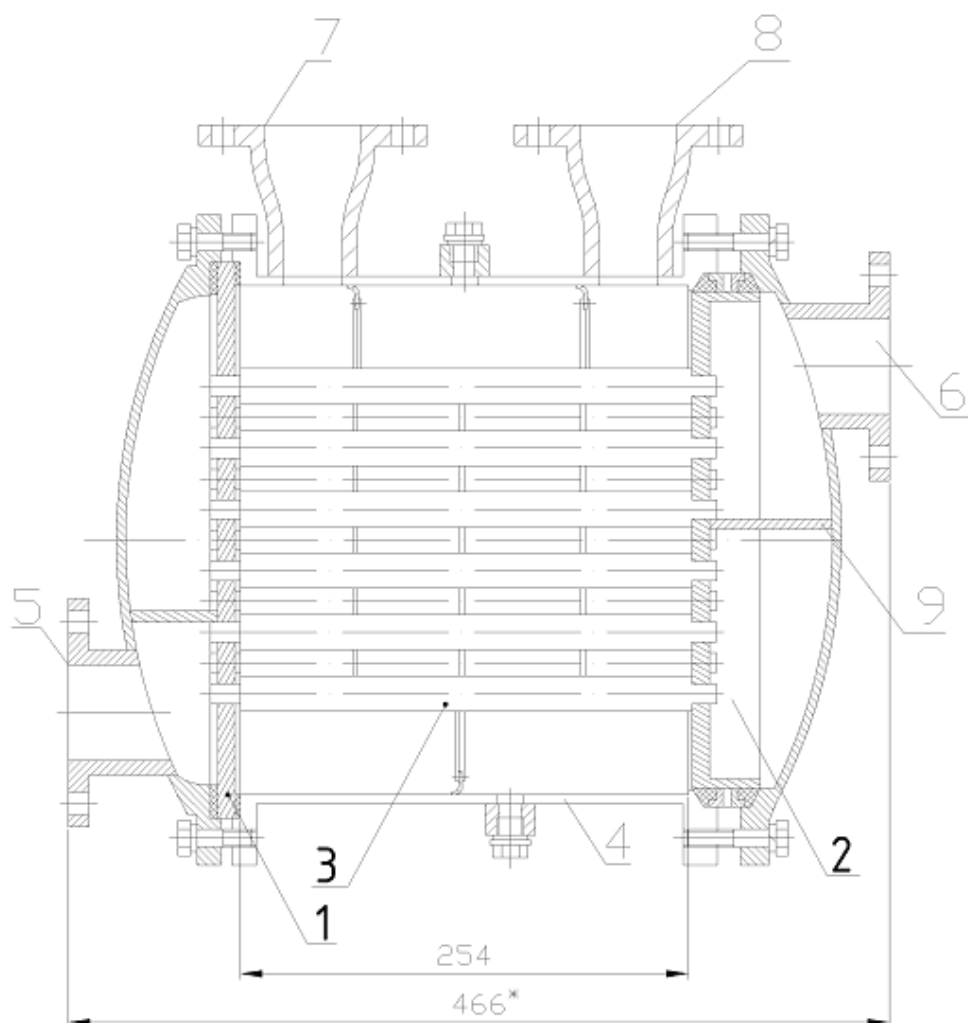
Охолоджувач масла: 1 – трубна дошка; 2 – поворотна секція; 3 – поверхня охолодження; 4 – корпус маслоохолоджувача; 5 – відвідний патрубок води; 6 – підвідний патрубок води; 7 – підвідний патрубок масла; 8 – відвідний патрубок масла; 9 – перегородка
